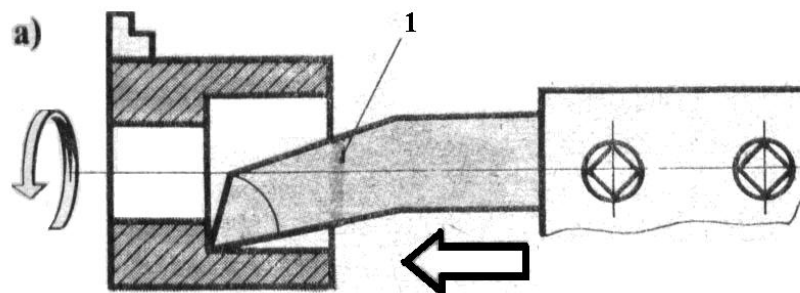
Схема розточування отвору розточувальним упорним різцем 1
